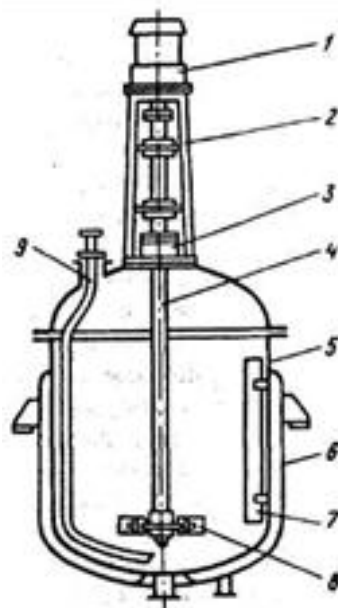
Реактор з лопатовою мішалкою 1 - привід; 2 - стійка приводу; 3 - ущільнення; 4 - вал; 5-корпус; 6 - сорочка; 7 - відбивна перегородка; 8 – лопатева мішалка; 9 – труба
